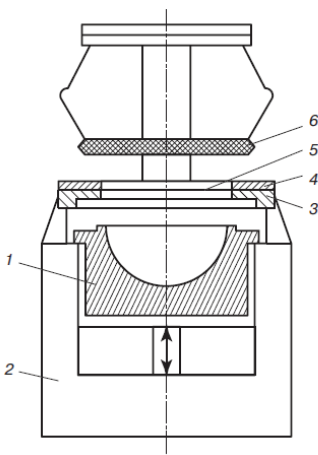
Принципова схема однопозиційної вакуумформувочної машини
